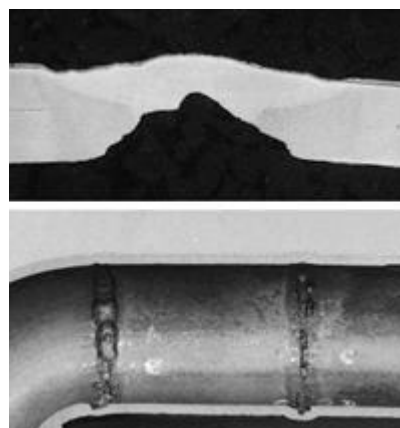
Corrosión selectiva en el material de aporte de una soldadura circunferencial.
